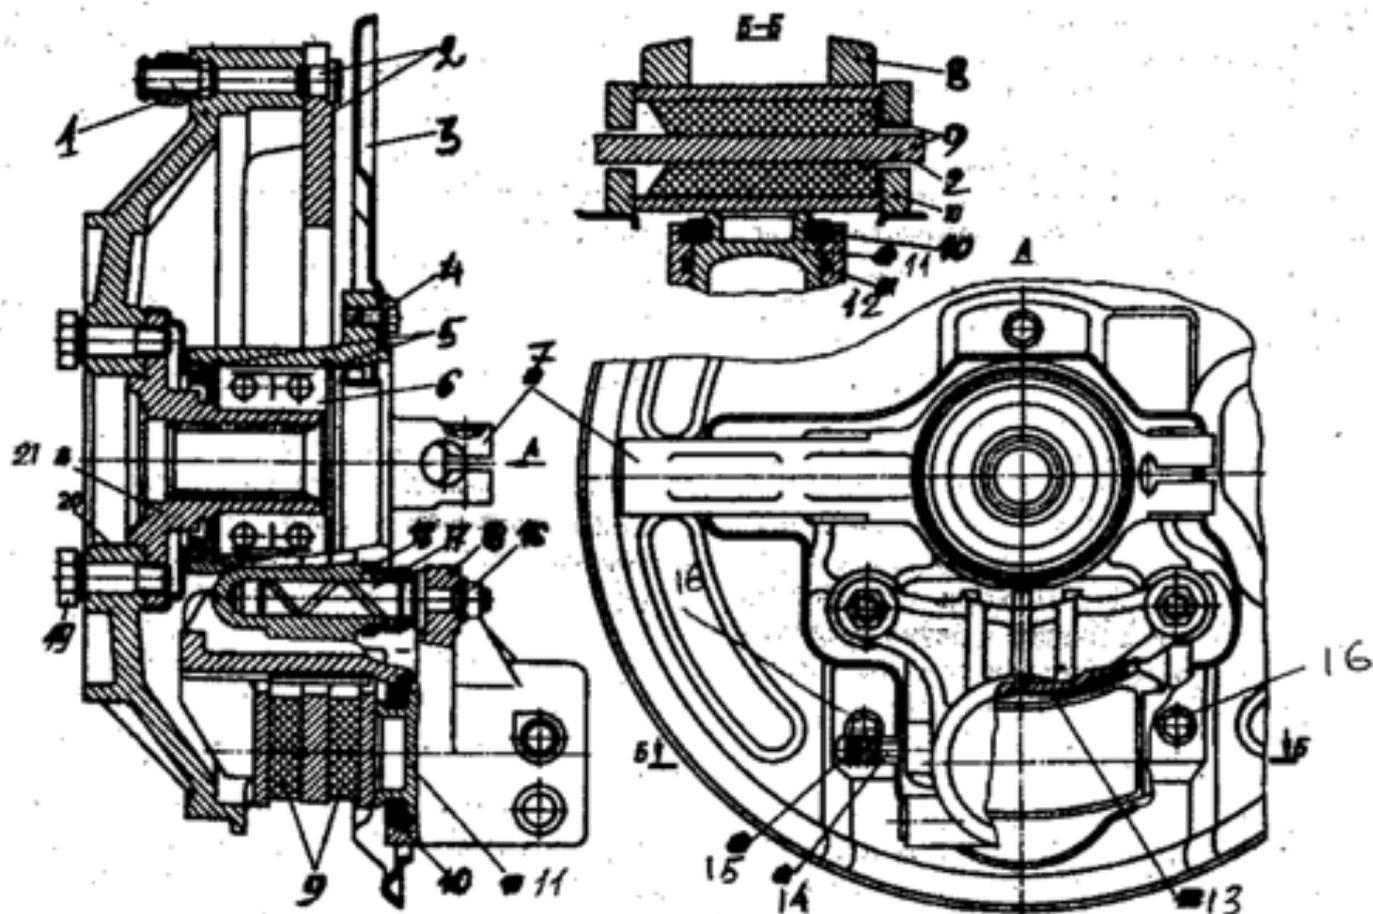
Тормоз передний с поворотным кулаком и ступицей: 1 - гайка крепления колеса; 2 - диск тормоза с болтами; 3 - кожух грязезащитный; 4 - болт крепления кожуха; 5 - кольцо стопорное; 6 - подшипник; 7 - кулак поворотный; 8 - скоба; 9 - колодка тормозная; 10 - чехол защитный поршня; 11 - поршень; 12 - кольцо уплотнительное поршня; 13 - пружина колодок; 14 - клапан выпуска воздуха; 15 - колпачок защитный; 16 - гайка крепления пальца; 17 - палец направляющий; 18 - чехол защитный; 19 - болт крепления фланца ступицы; 20 - фланец ступицы; 21 - ступица.
